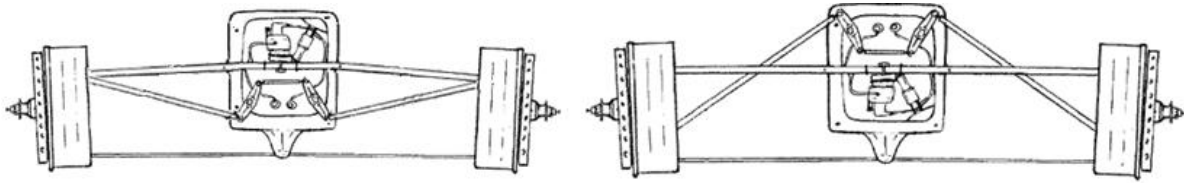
Pull rod imagen izquierda, Push rod imagen derecha
